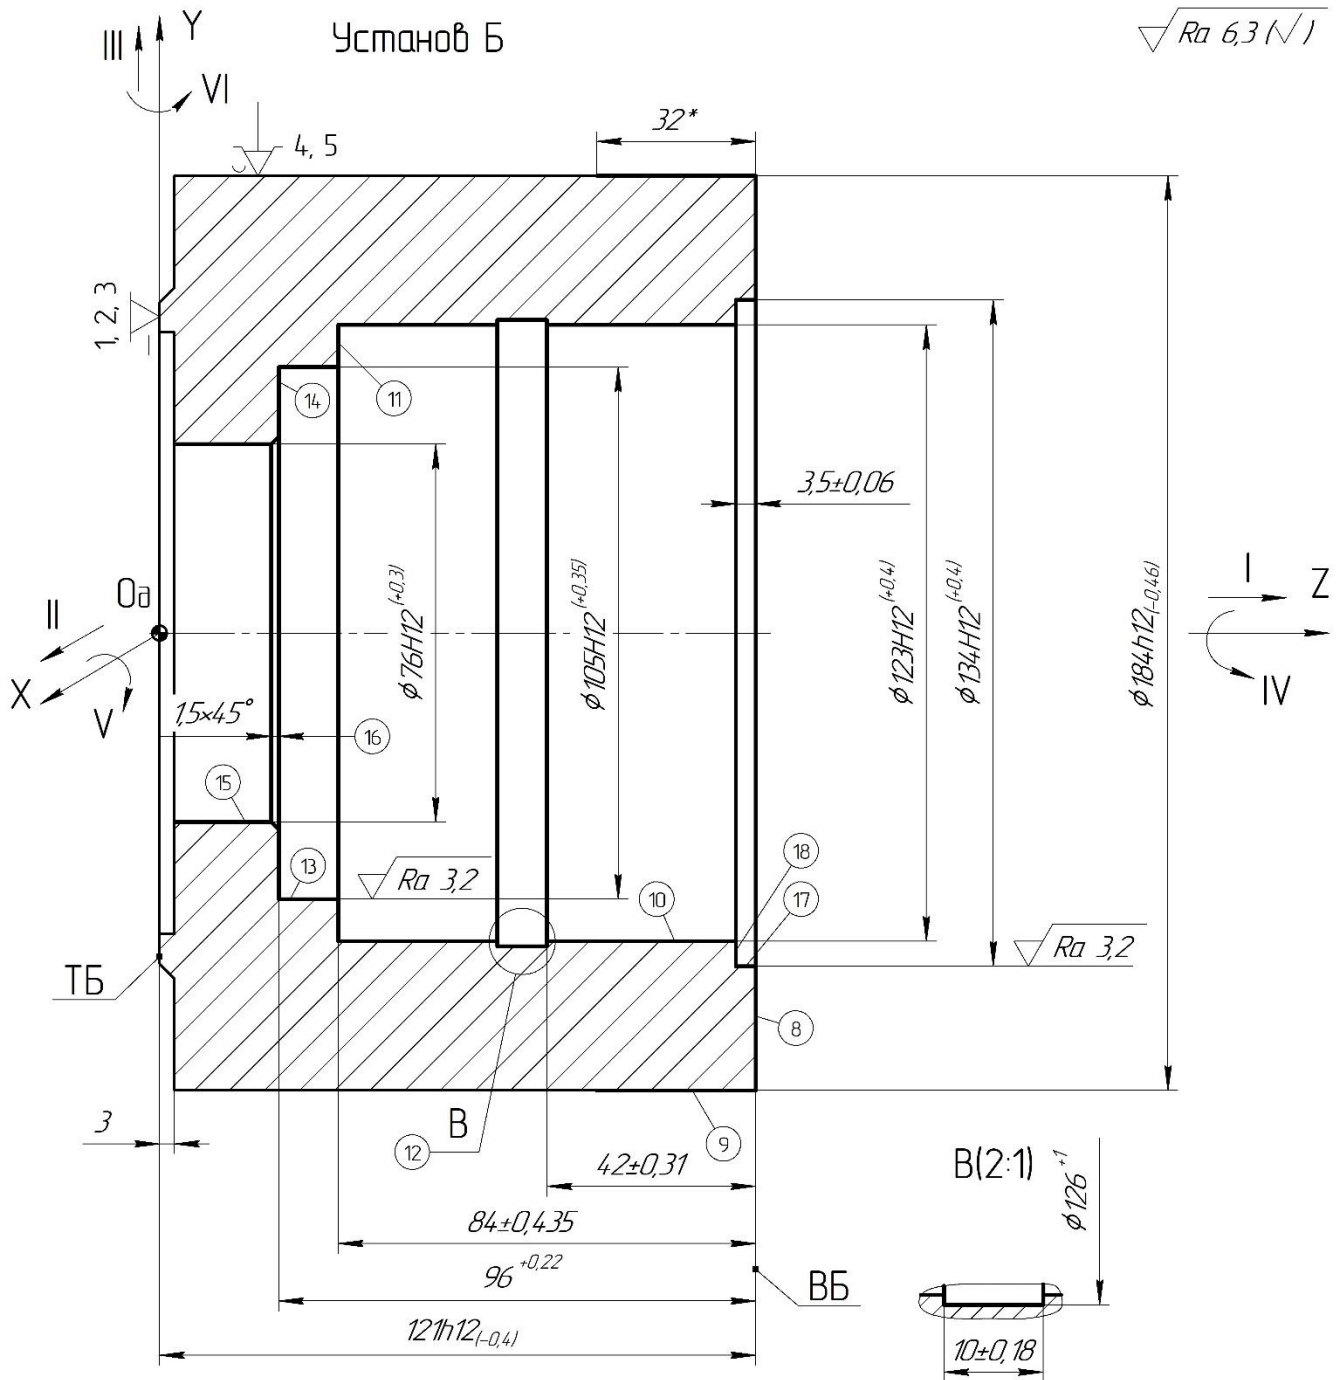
Схема установки заготовки на операції 015 «Токарна з ЧПК».
